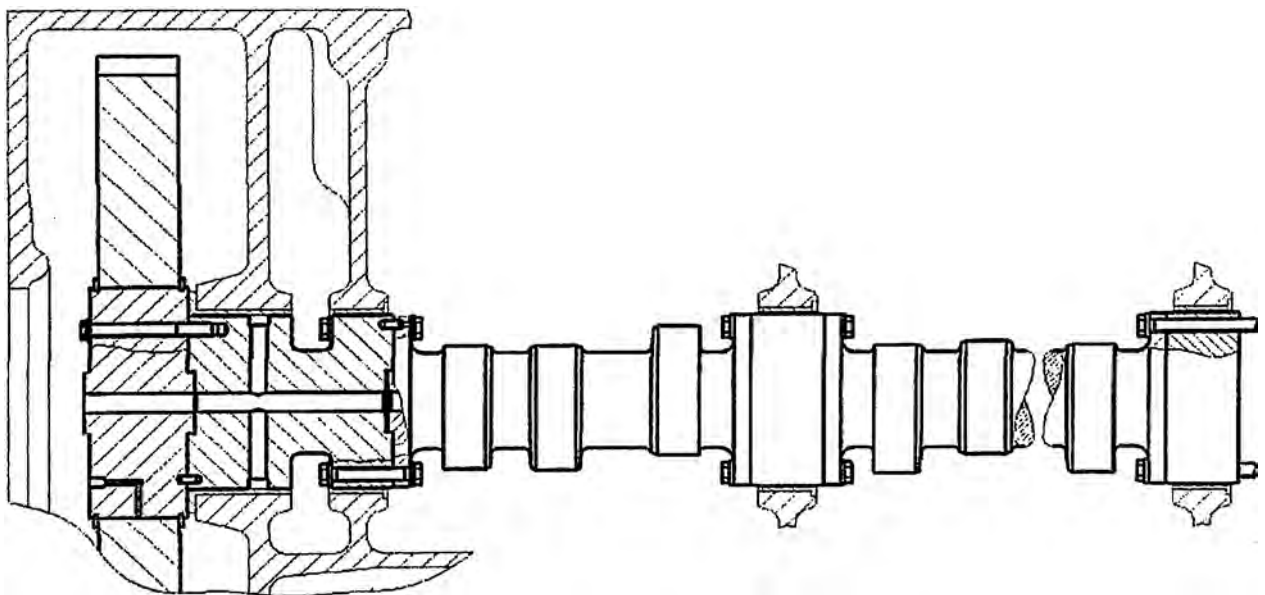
Vista de 1ra y 2da sección de eje de levas
